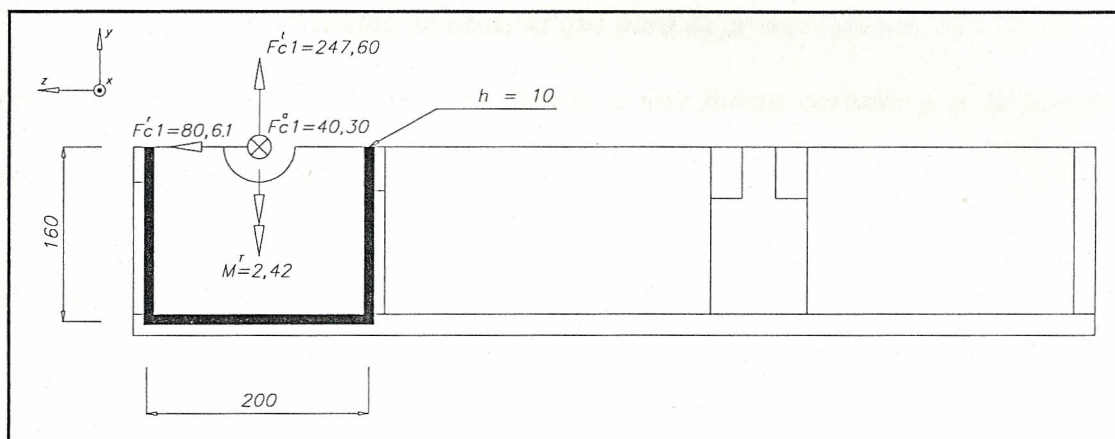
Fuerzas y dimensiones en el 1° cordón de soldadura de la plancha 1.
